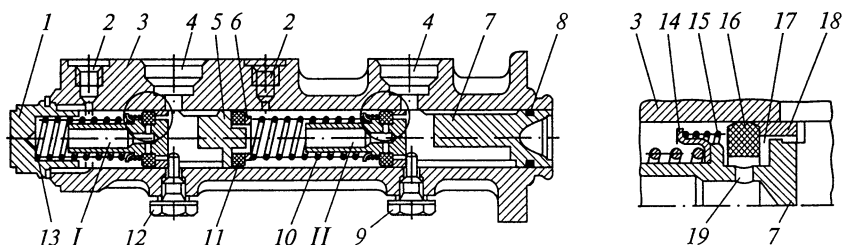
Главный тормозной цилиндр легковых автомобилей ВАЗ:
